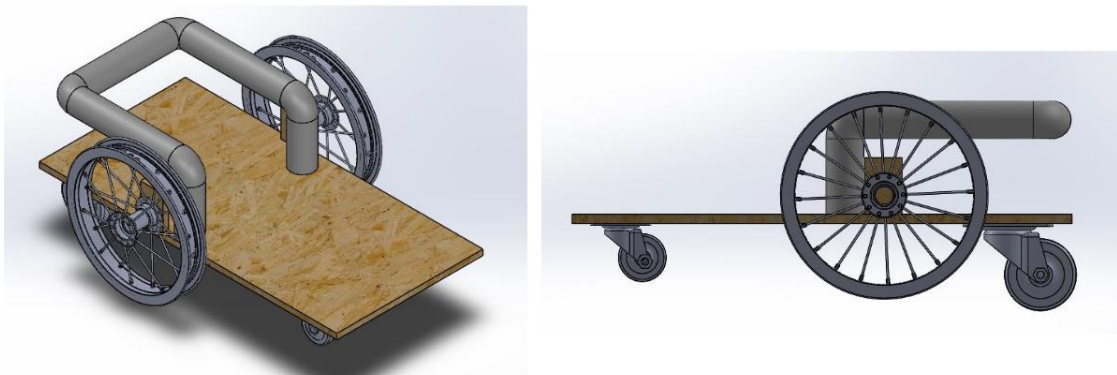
Desenho técnico da cadeira de rodas infantil planejada pelo grupo.
